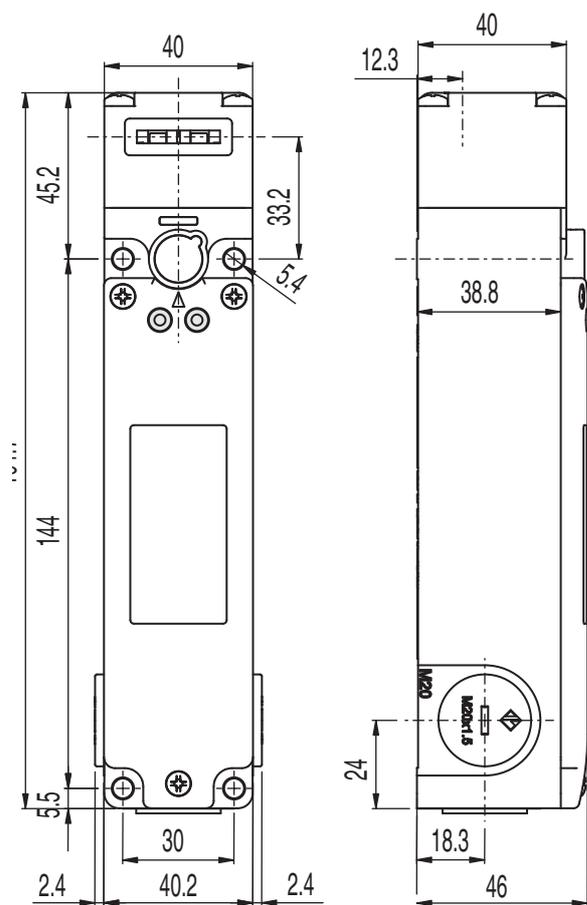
Dimensiones del L200-M1C3-MLM24-L2G en mm
